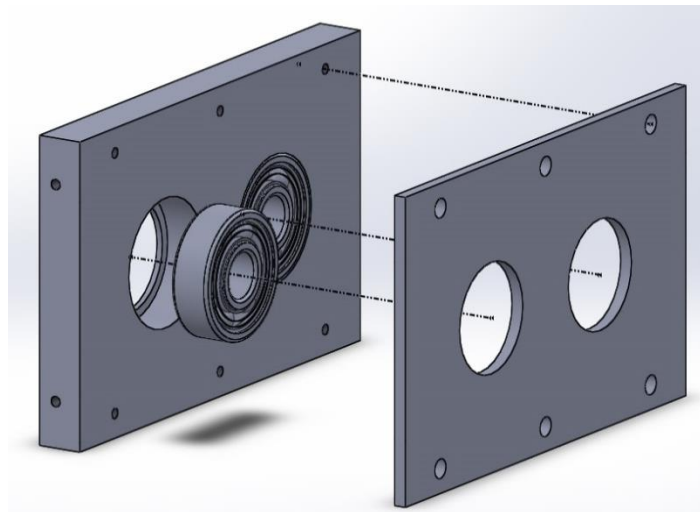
11 Ensamblaje de la caja de rodamientos.
